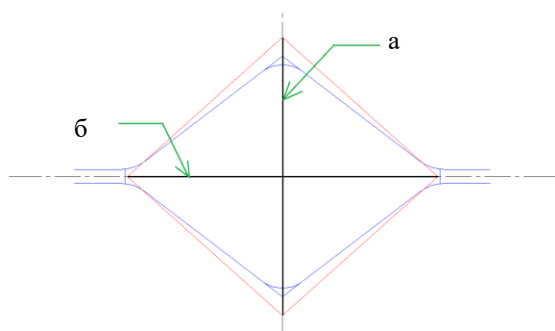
Совпадение малой (а) и большой (б) диагоналей заготовки и калибра
